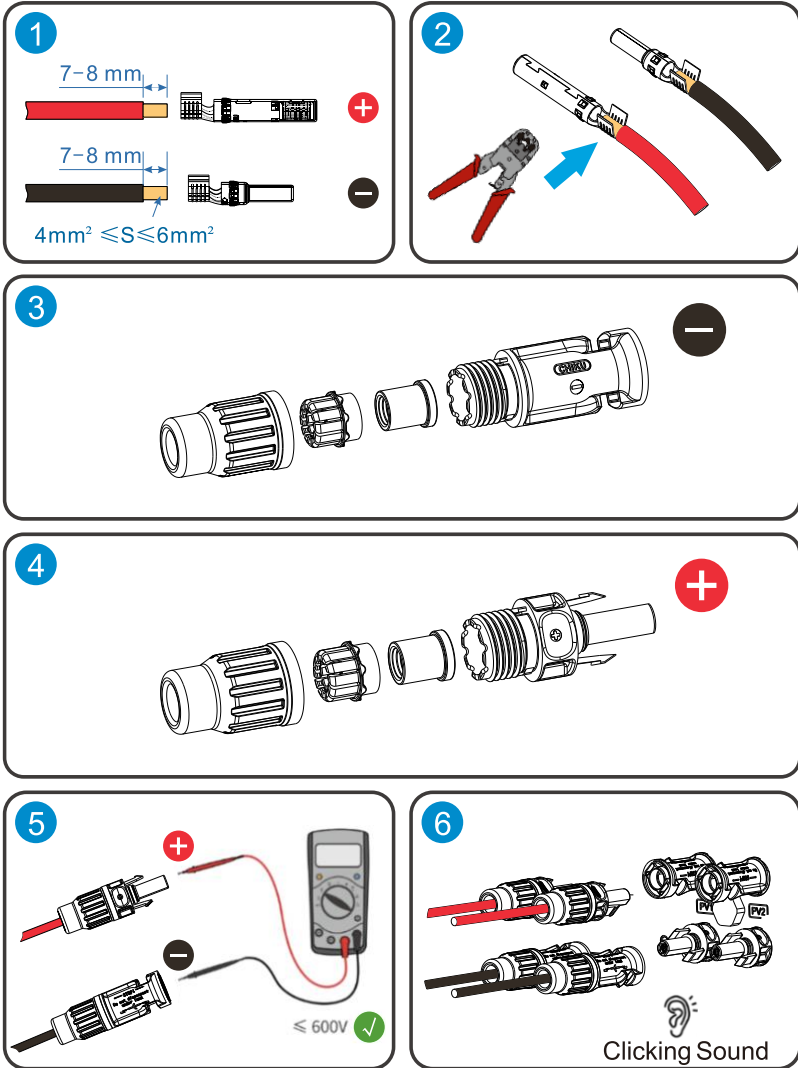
Passaggi per l'installazione e il collegamento del cavo DC
